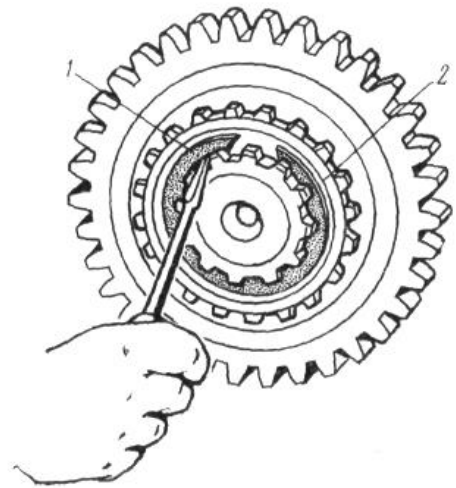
Знімання стопорного кільця веденої шестерні понижуючого редуктора: 1- стопорне кільце; 2- ведена шестерня
